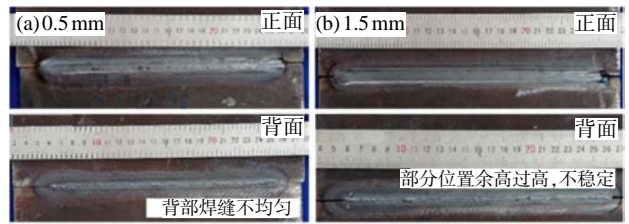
不同装配间隙条件下 K-TIG 焊缝表面成型
